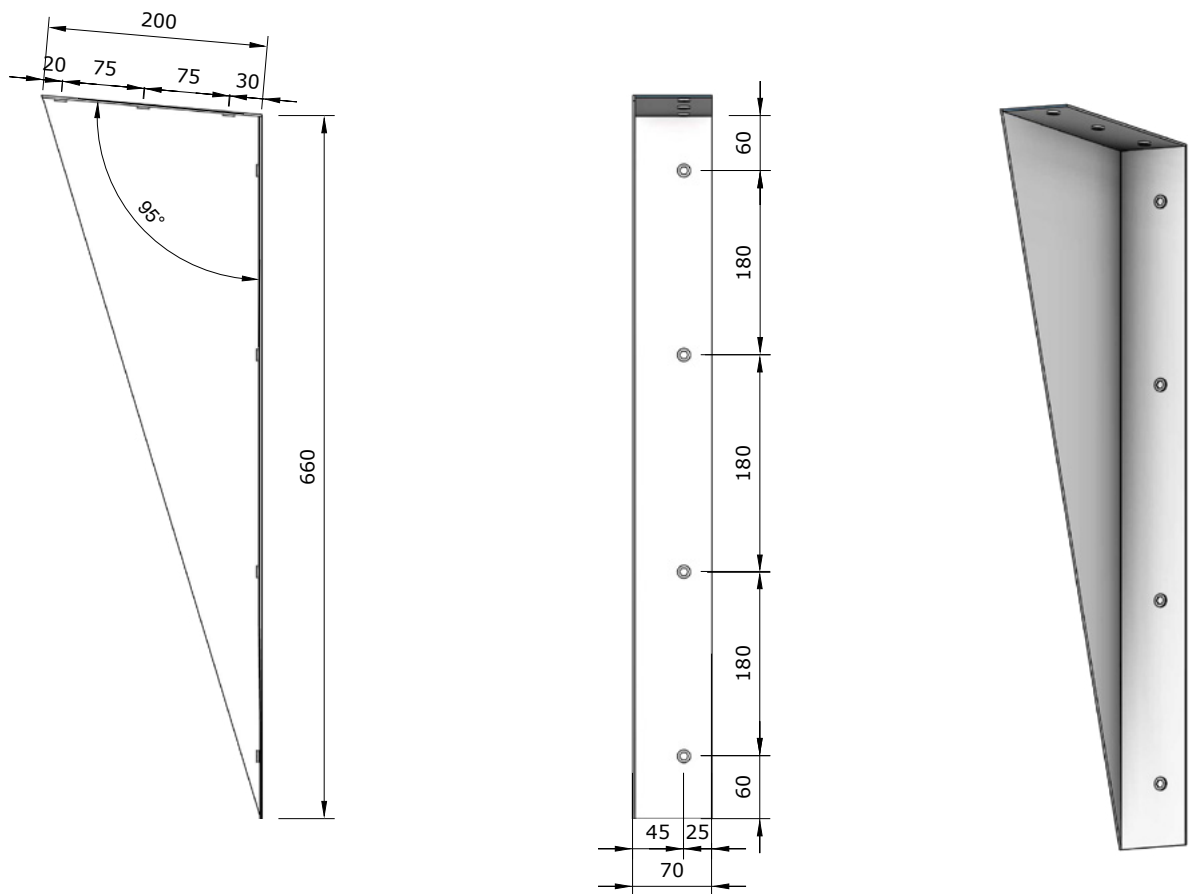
Vues de la tôle de support avec les dimensions de la fixation, dimensions en mm.
